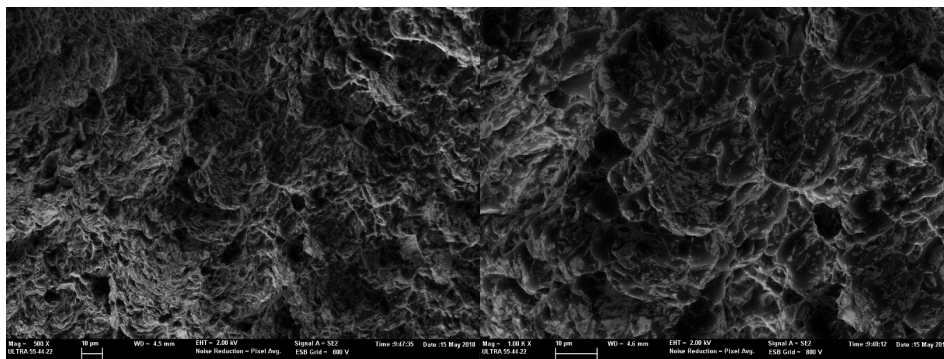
Análisis de fractura en la zona de fractura final de la muestra ZY.
